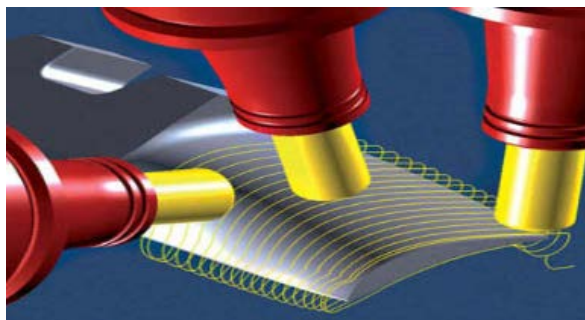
Usinage en bout d'aube de turbine 5 axes [32].
